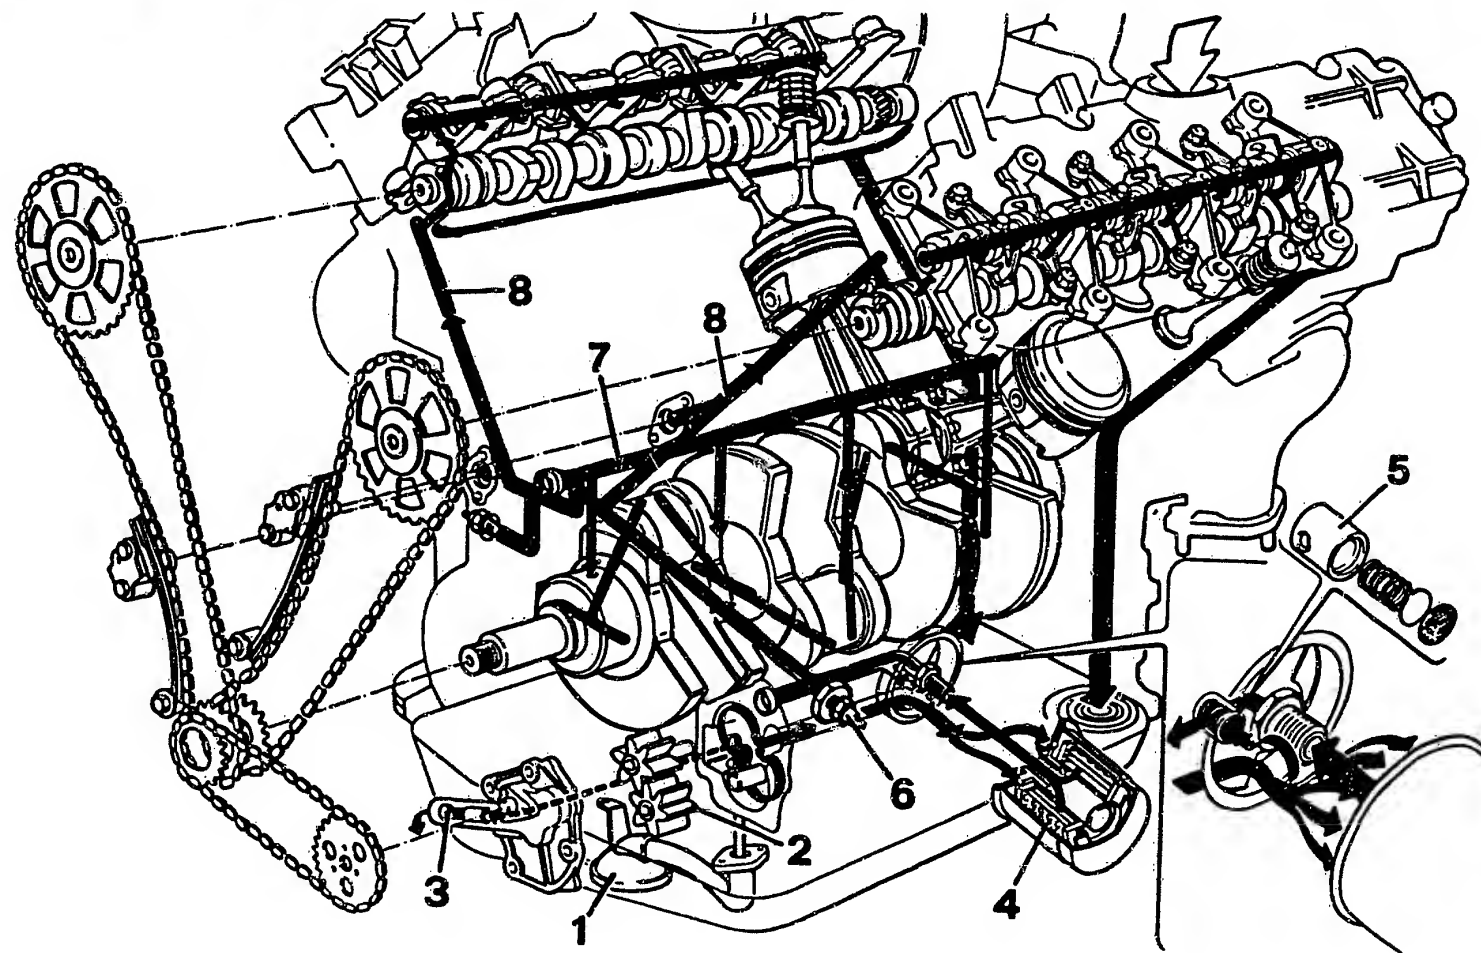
2850 V6-Motor: Schwimmersystem mit 1 Ansaugsieb – 2 Ölpumpe – 3 Überdruckventil – 4 Ölfilter im Hauptstrom – 5 Umgehungsventil – 6 Öldruckschalter – 7 Hauptkanal – 8 Steigleitungen zu den Zylinderköpfen.
